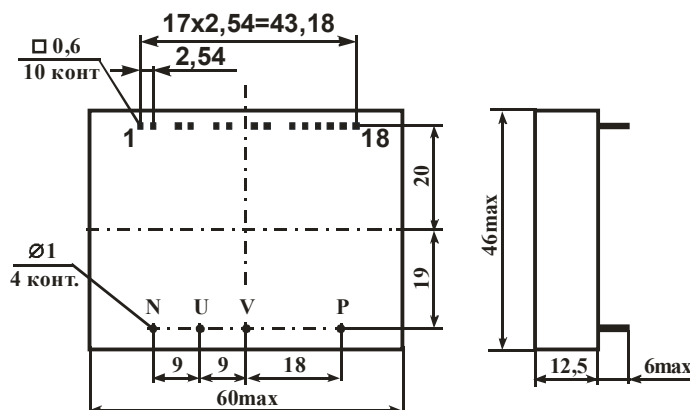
Габаритный чертеж модулей M13B-1-6-ПП4
